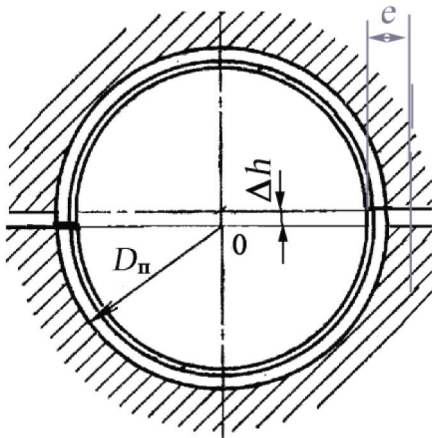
Схема установки вкладышей в кривошипной головке шатуна: D_n – диаметр постели; Δh – выступание вкладыша; e – осевая нагрузка для закрытия стыка
